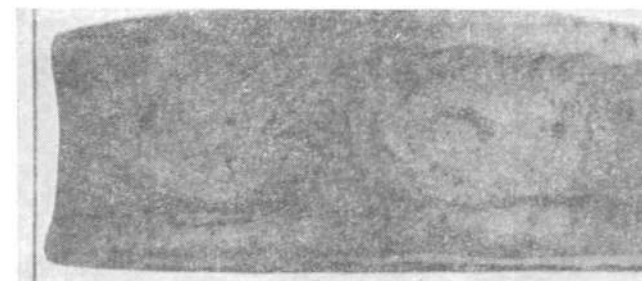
Внешний вид шва, выполненного автоматической сваркой под влажным флюсом (темные точки — поры).
